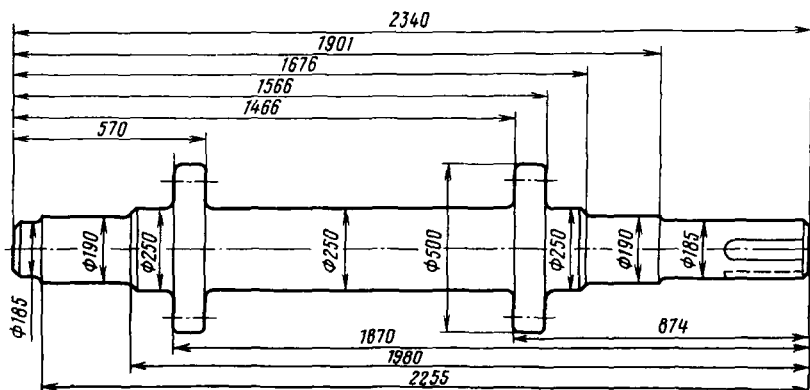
Главный приводной вал эскалатора ЭМ-1
